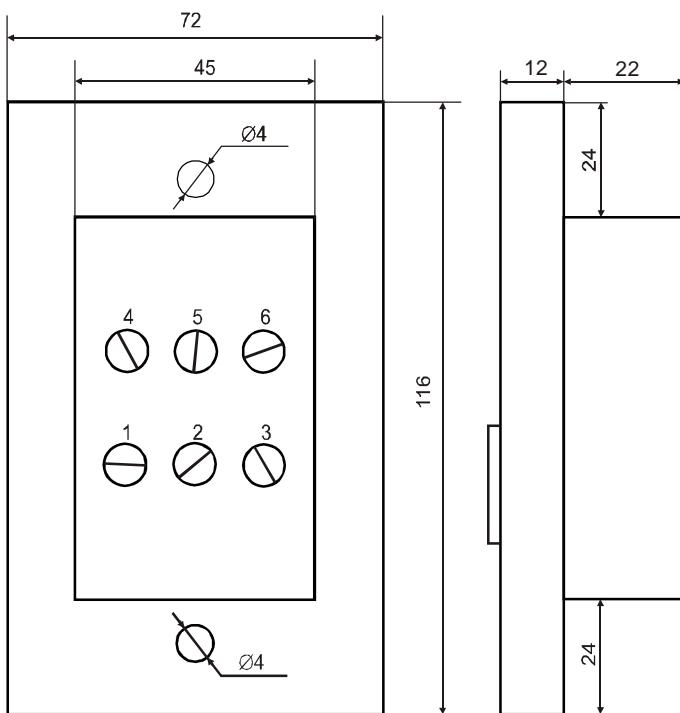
Габаритные размеры и расположение крепежных отверстий
